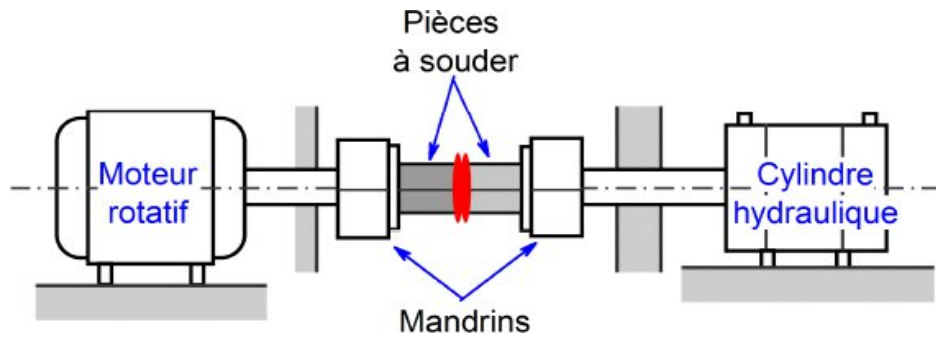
Processus du soudage par friction rotative à entraînement direct [7]
